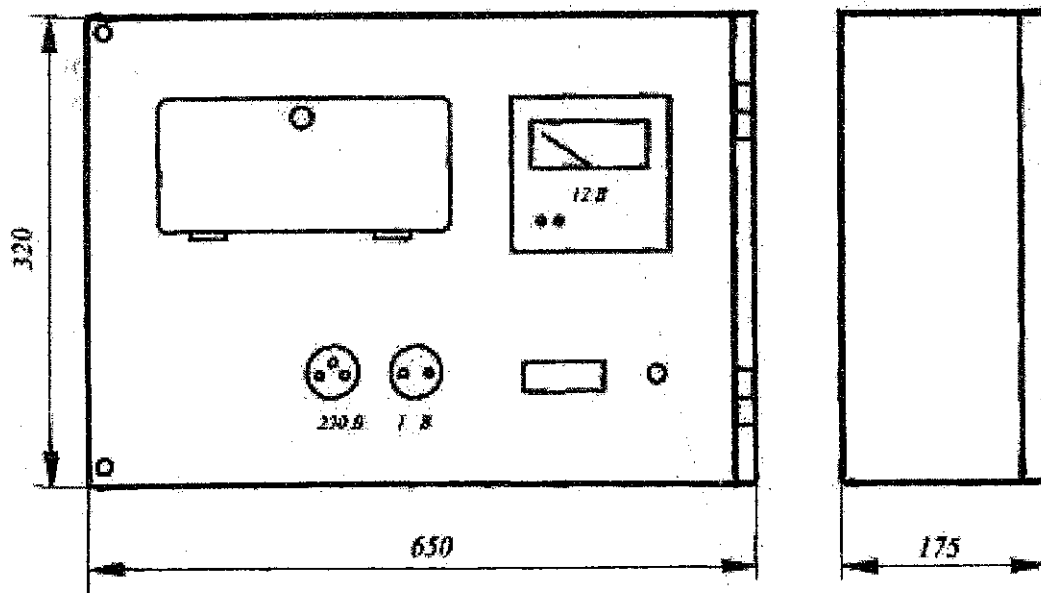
Габаритные размеры щитка гаражного ЯВУ-1Г-40-ЗУ
